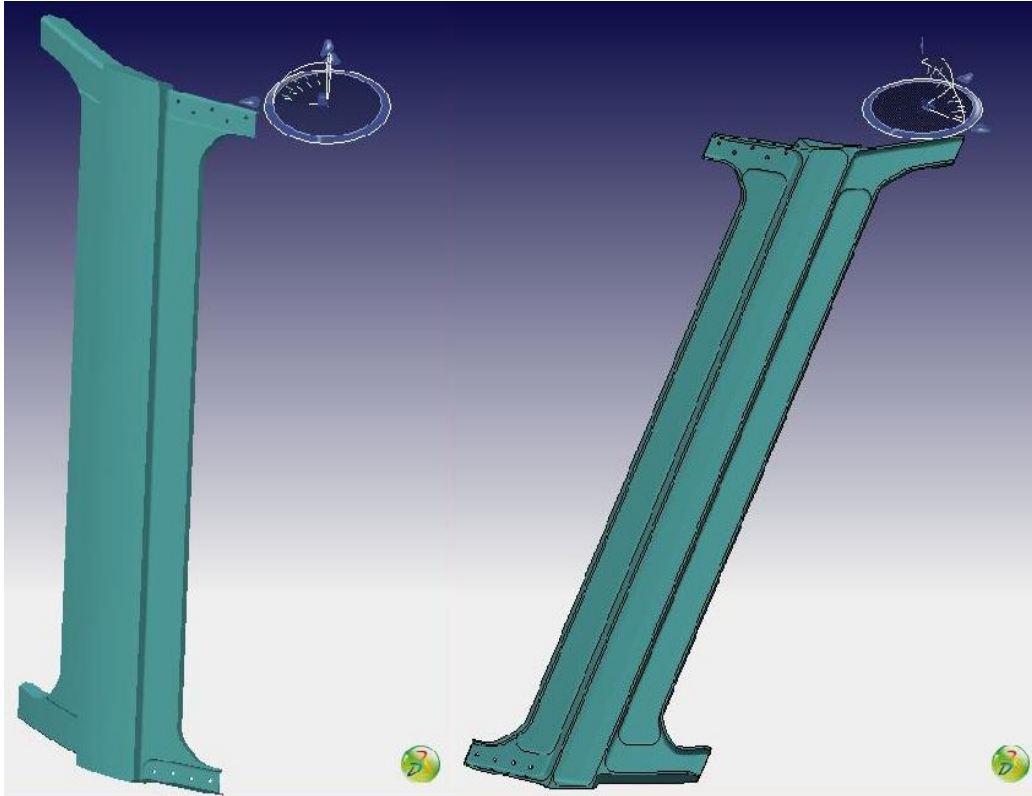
Proposta de alteração da viga lateral da estrutura.
